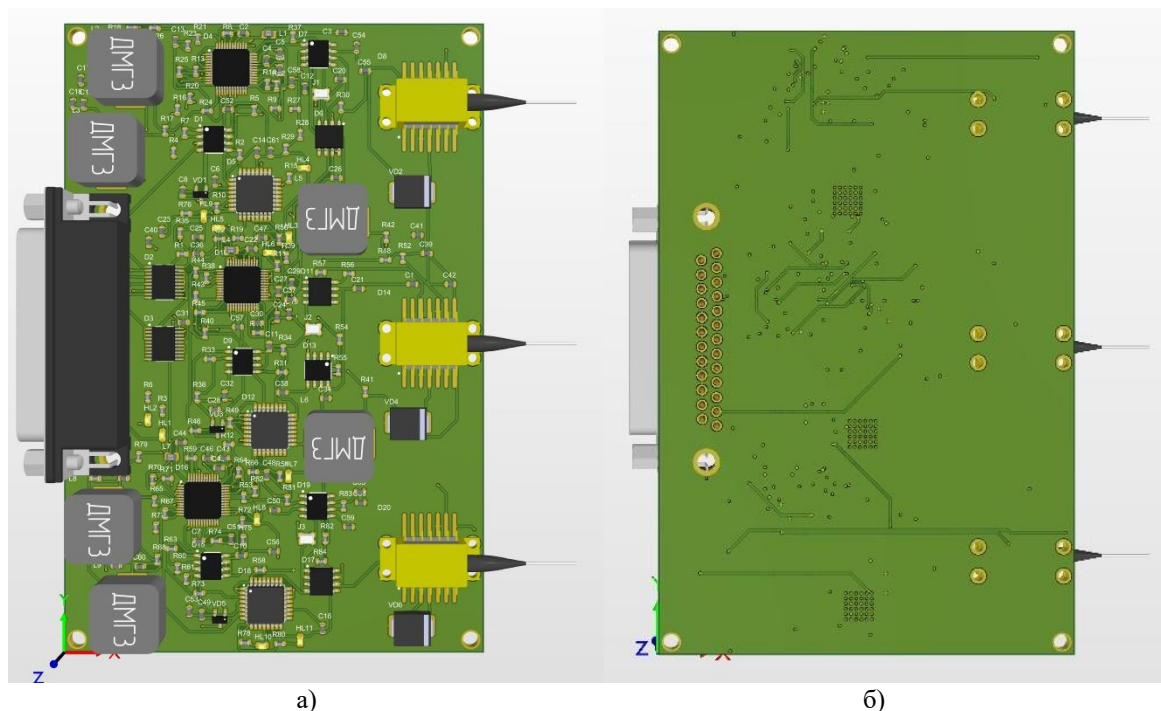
Печатный узел усилителя: вид сверху (а), вид снизу (б)
